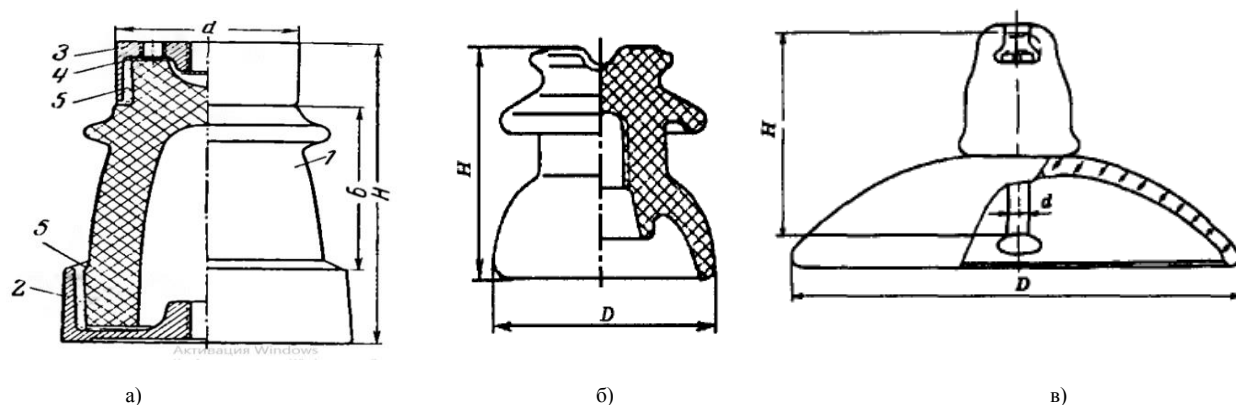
Конструкционный вид фарфоровых изоляторов, предназначенные для использования во внешней среде: а) опорный изолятор типа ОФ -750кр: 1-тело фарфора, 2-фланец, 3-колпачок, 4-прокладка, 5-цементная связка; б) линейный стержневой изолятор; в) подвесной изолятор со сферической поверхностью
